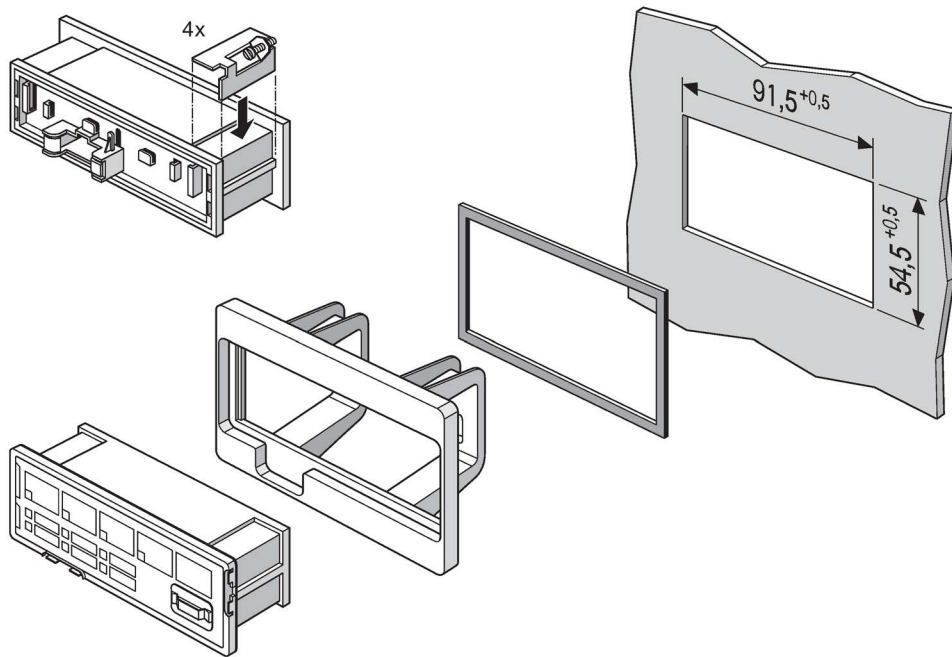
Montaje del adaptador para el módulo de mando (1)
